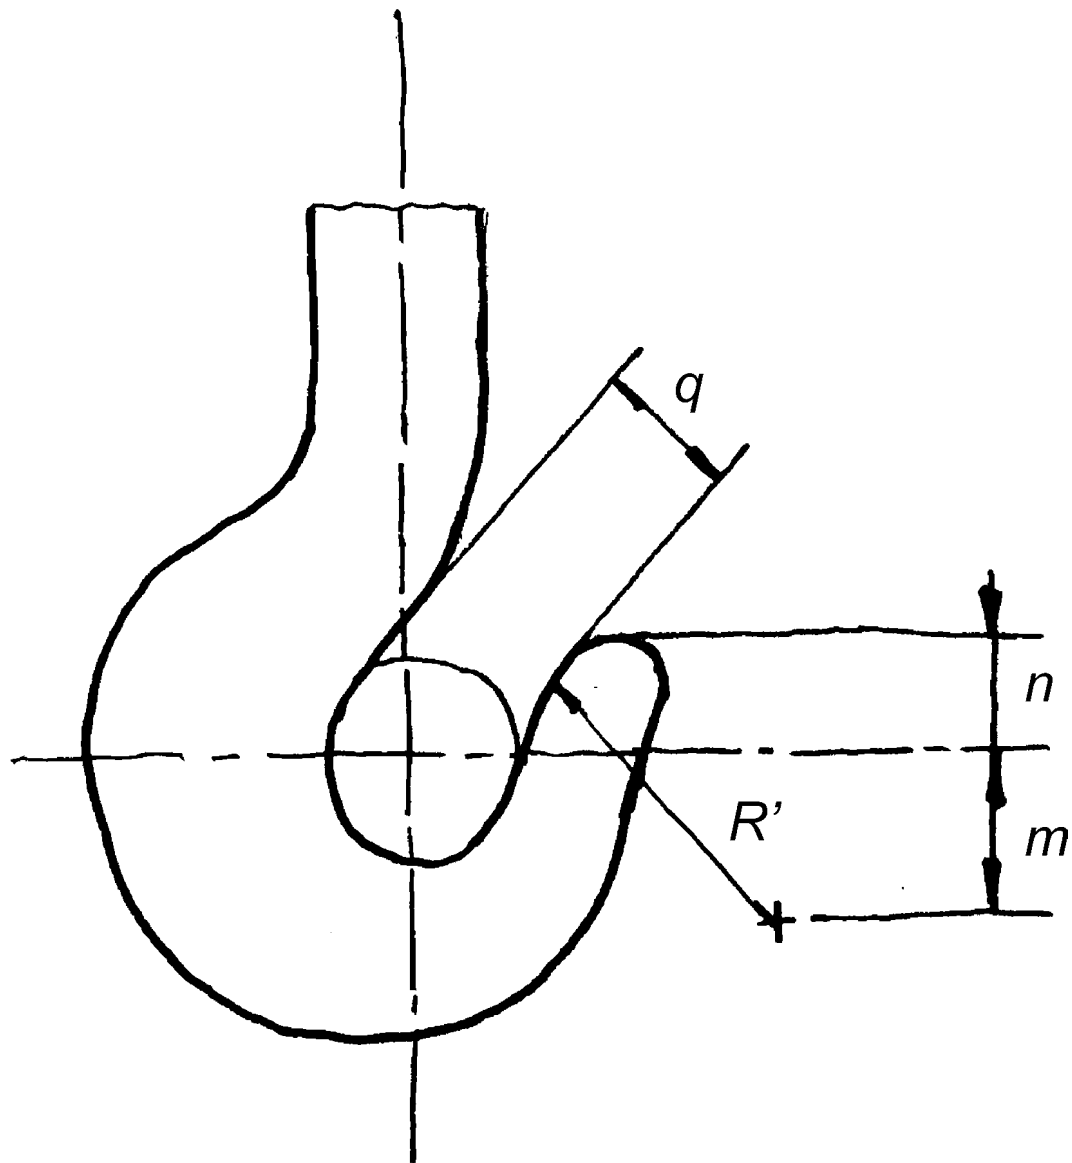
Altre dimensioni del gancio ad un becco.
